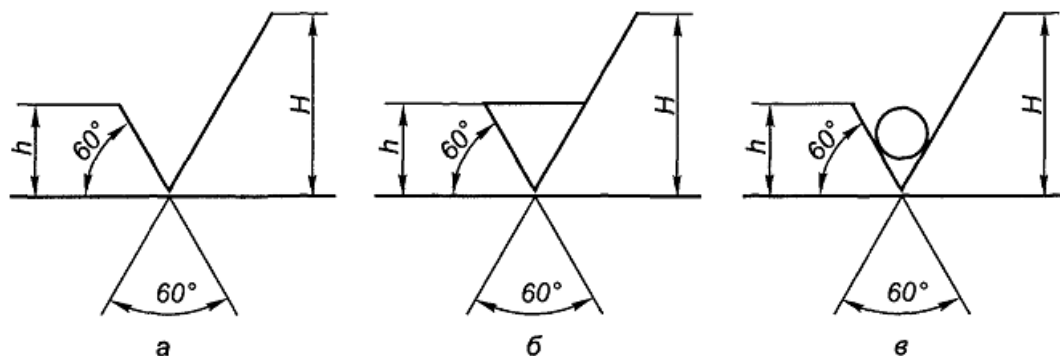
Знаки шероховатости поверхности полученной: без указания способа получения поверхности (а), резанием (б), литьем (в)
